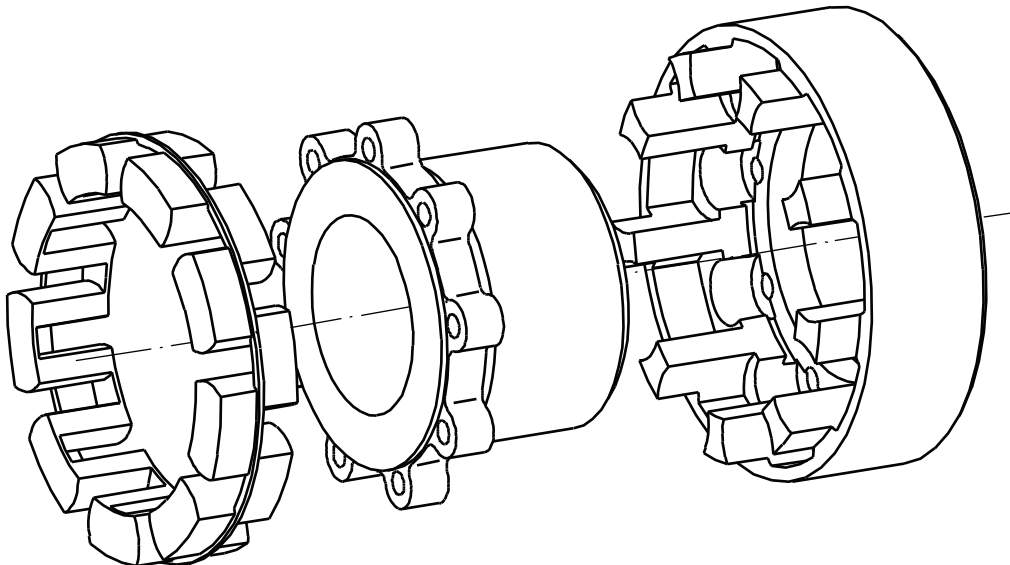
Beispiel für eine Technische Zeichnung als Explosionszeichnung (Kupplungsflansch nach Bild 2-6)
